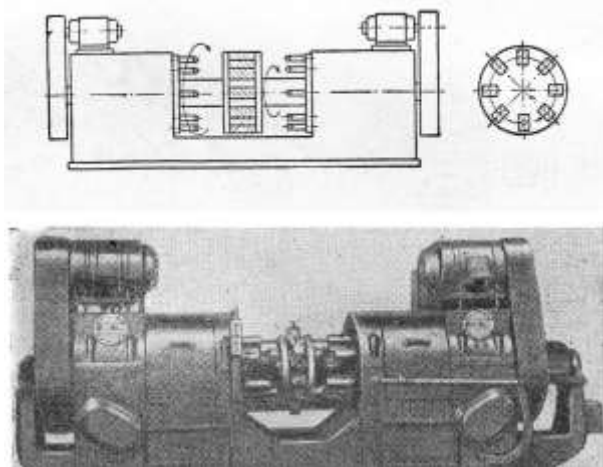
Компоновка агрегатного станка с несколькими горизонтальными головками и вертикальным круговым перемещением заготовок
